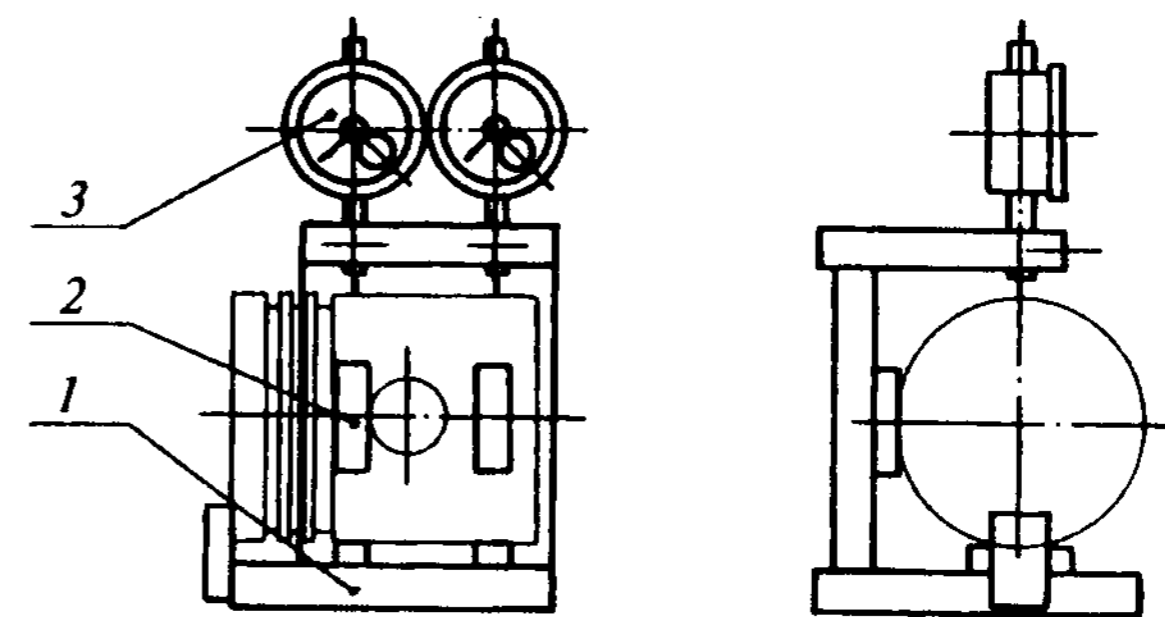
Прибор для измерения размеров, эллипсоидности юбки поршня
